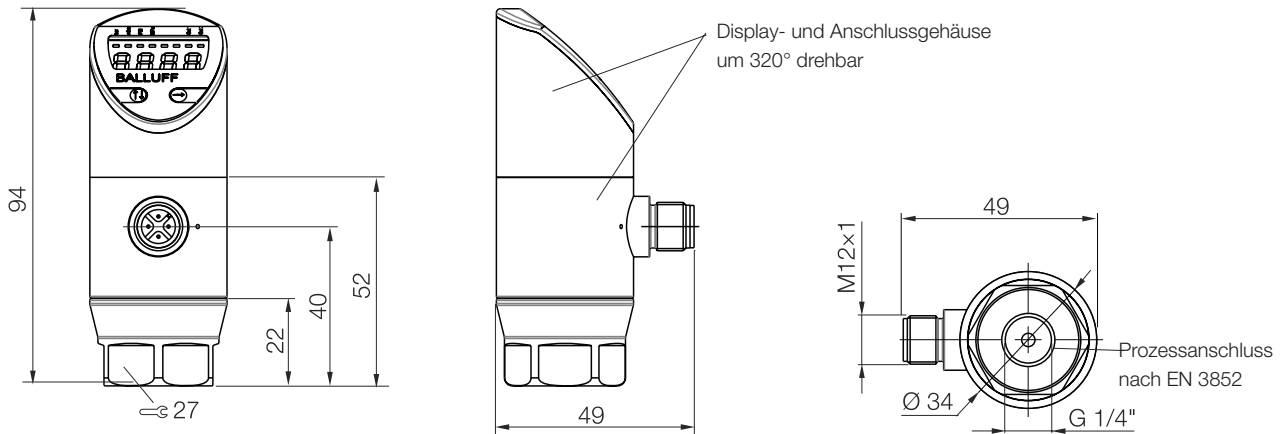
Maßzeichnung Standard- und High-End-Drucksensor, nicht frontbündig
